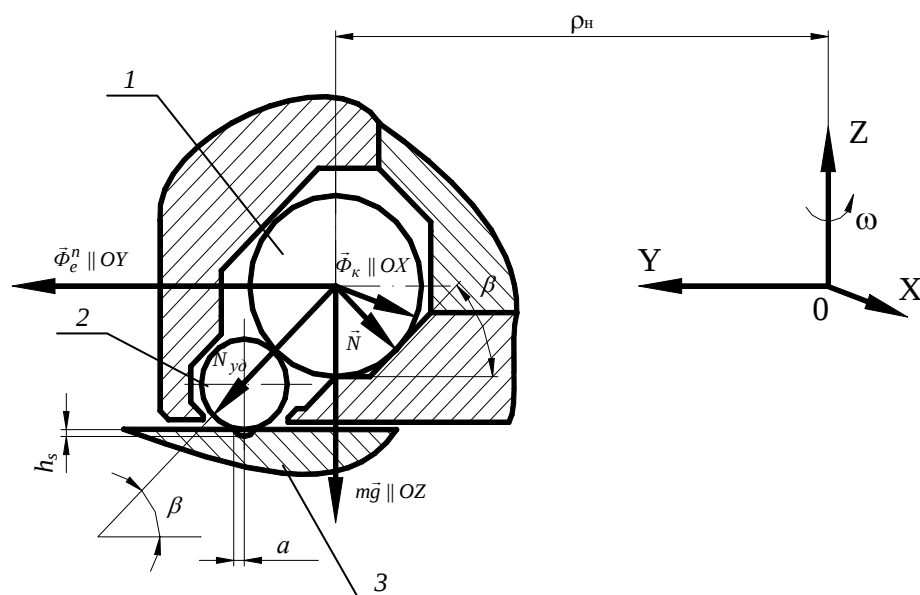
Схематическое сечение кольцевого канала движения шаров в рабочей зоне инструмента: 1- шар-ударник; 2 – шар-боек; 3 – обрабатываемая поверхность
